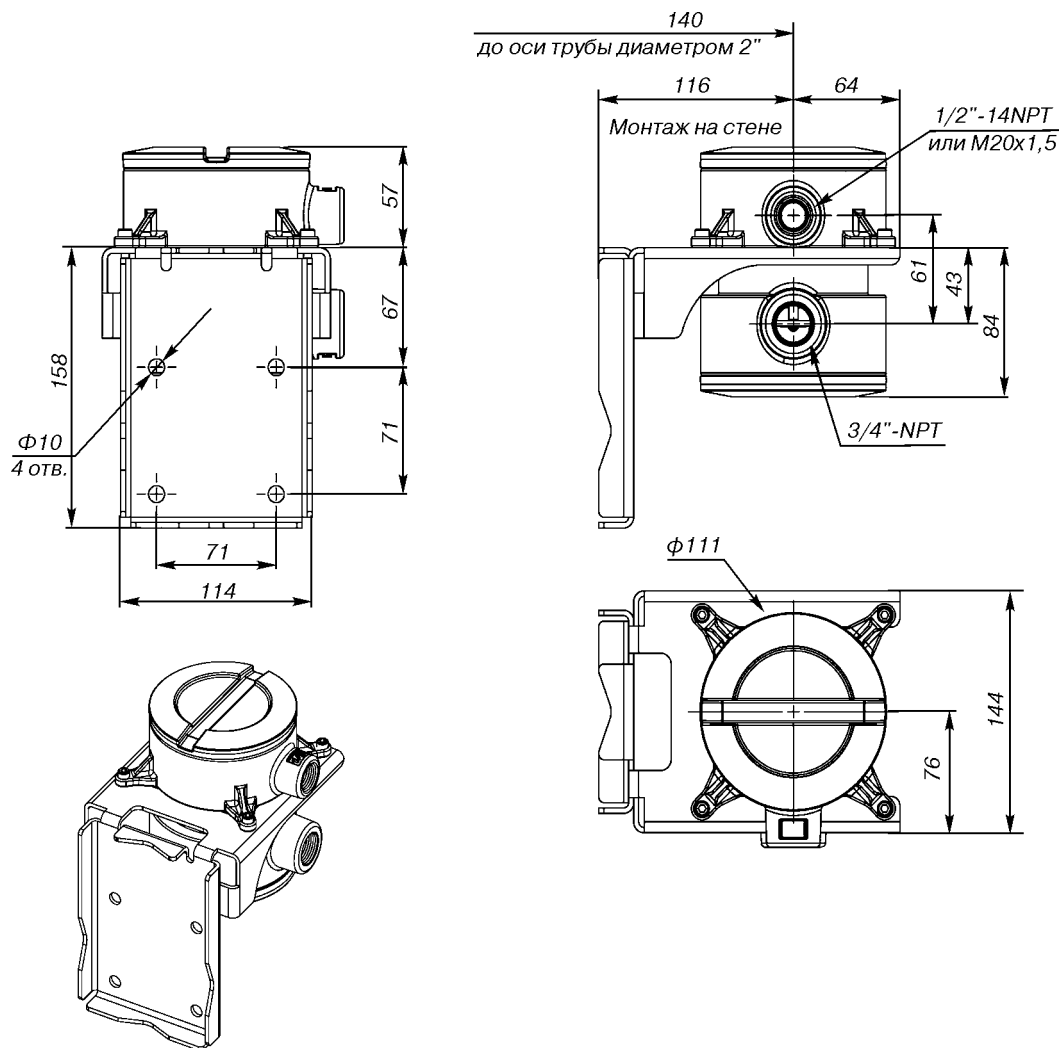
Габаритные и присоединительные размеры основного процессора при удаленном монтаже.
